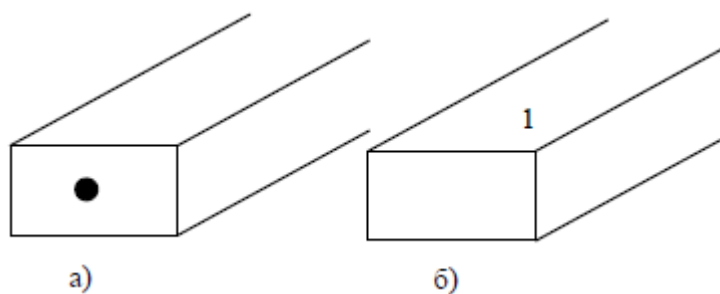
Схема маркировки доски (заготовки) на торце (а), на пласти (б)
